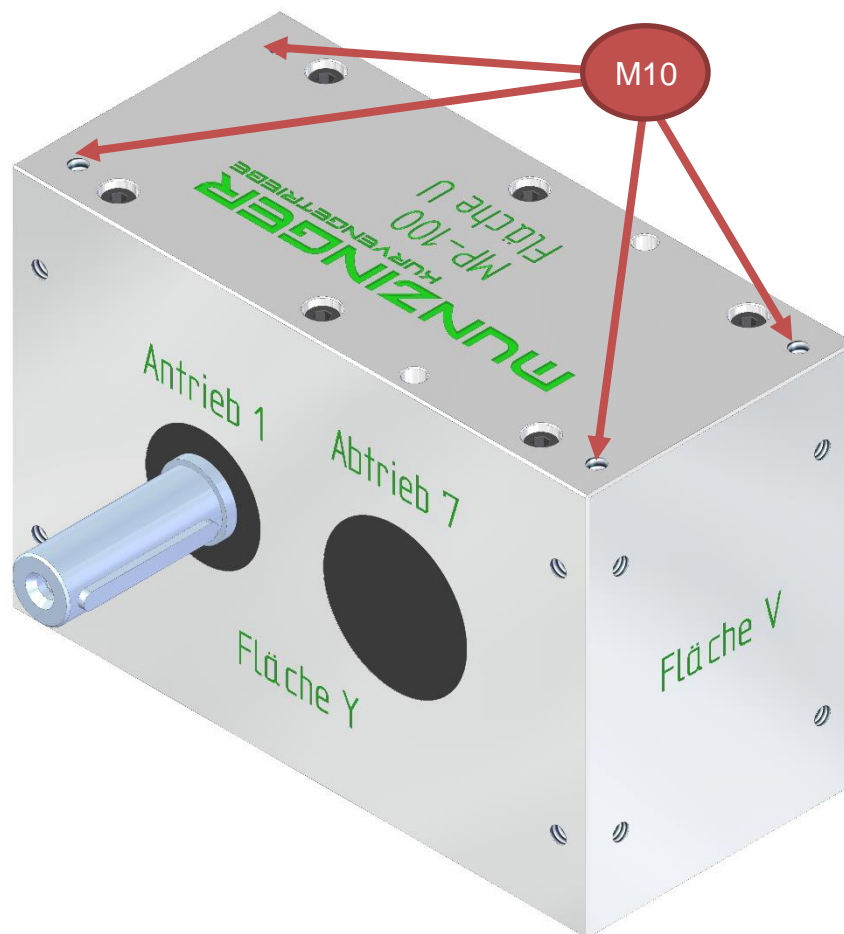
Gewindebohrungen für die Anschlagmittel
